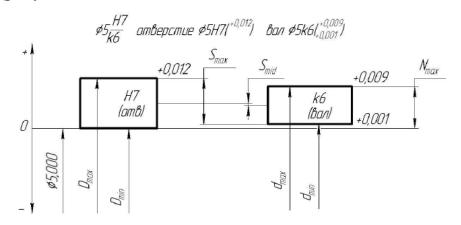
Схема расположения интервалов допусков посадки Тип посадки: переходная посадка в системе отверстия
